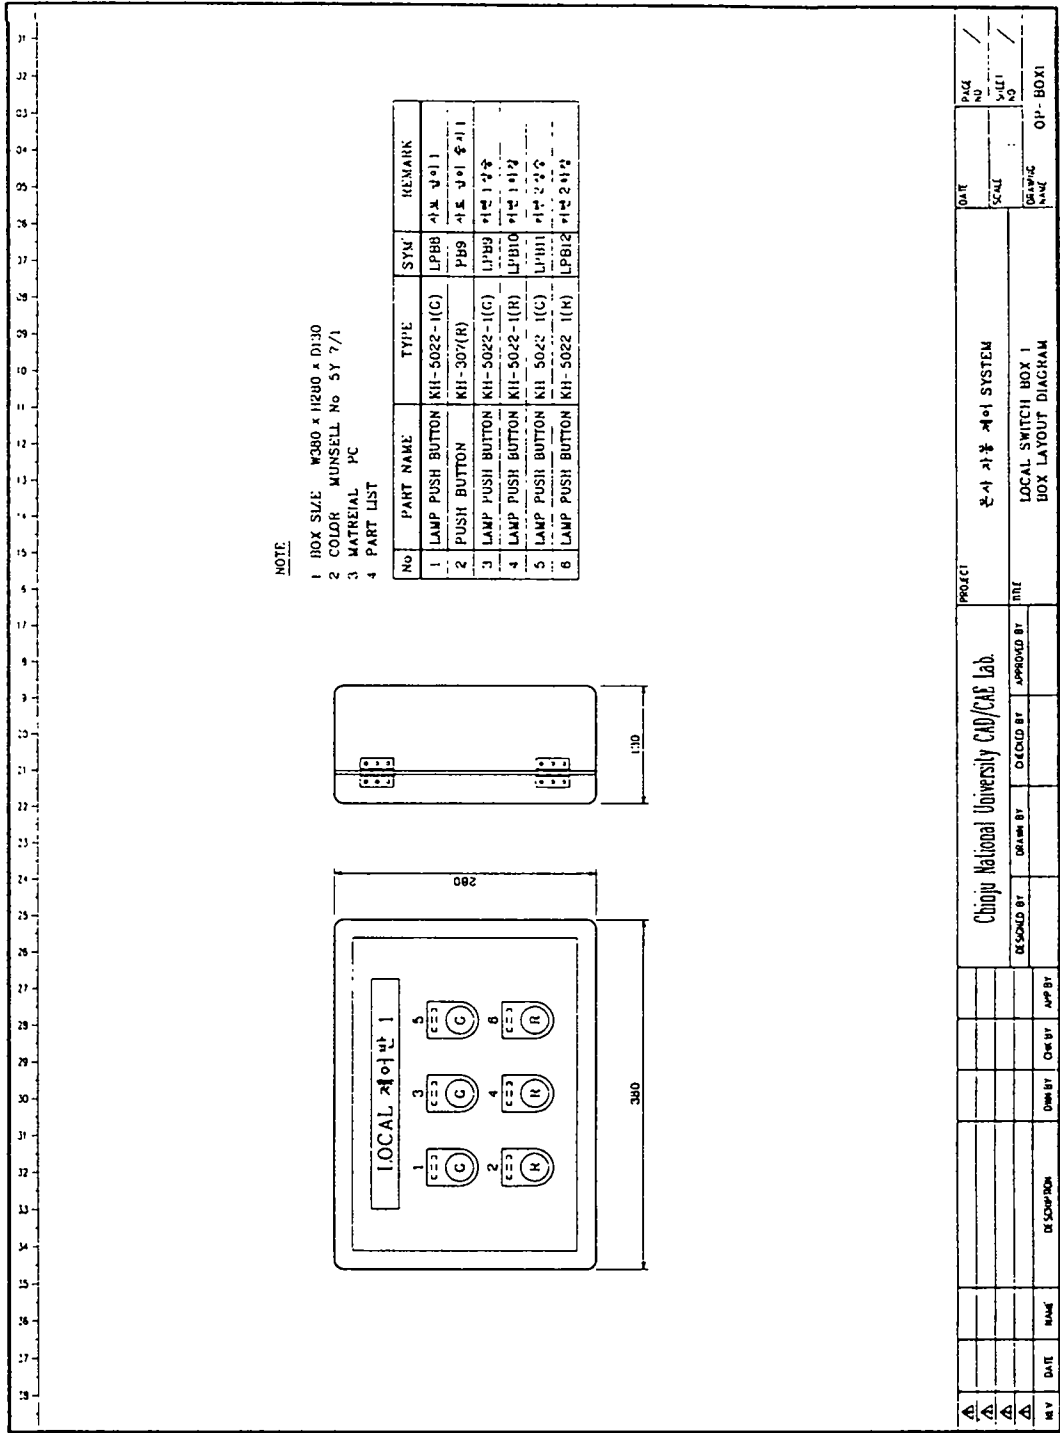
스위치 박스 배치도(Local switch box layout diagram) #1
